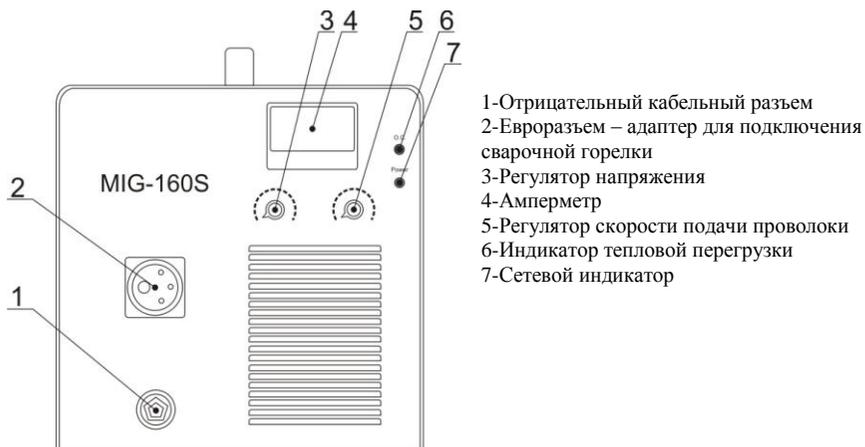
Полуавтомат сварочный MIG-160S
